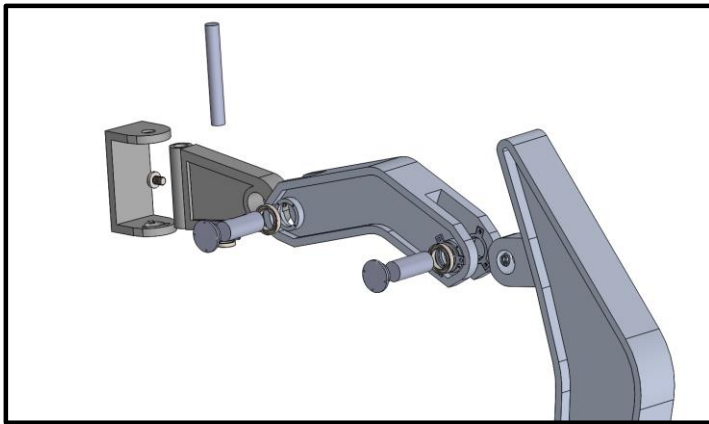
Vista Explosionada de Ensamblaje de Una Extremidad Completa
